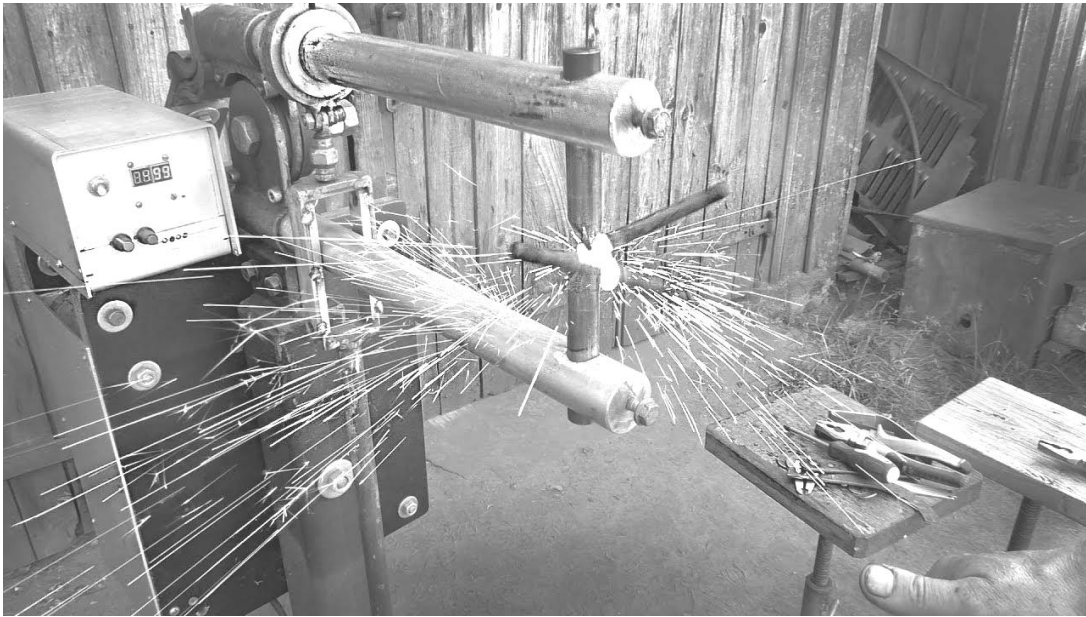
Загальний вигляд контактної точкової зварювання
